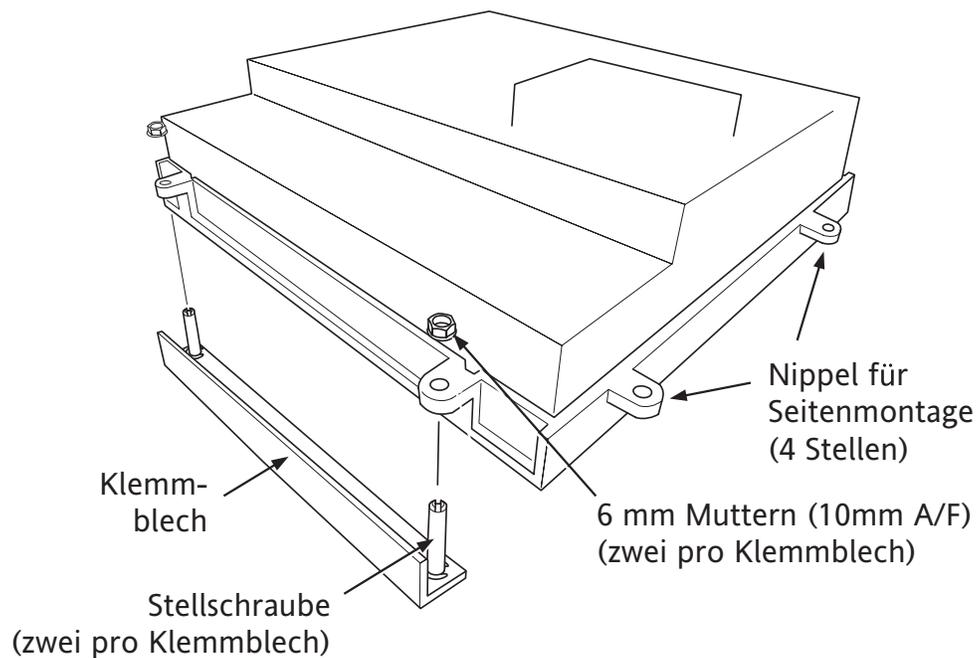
Details zur Befestigung der Klemmbleche
